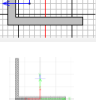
a) Plano inferior del puente. b) Plano superior del puente.
